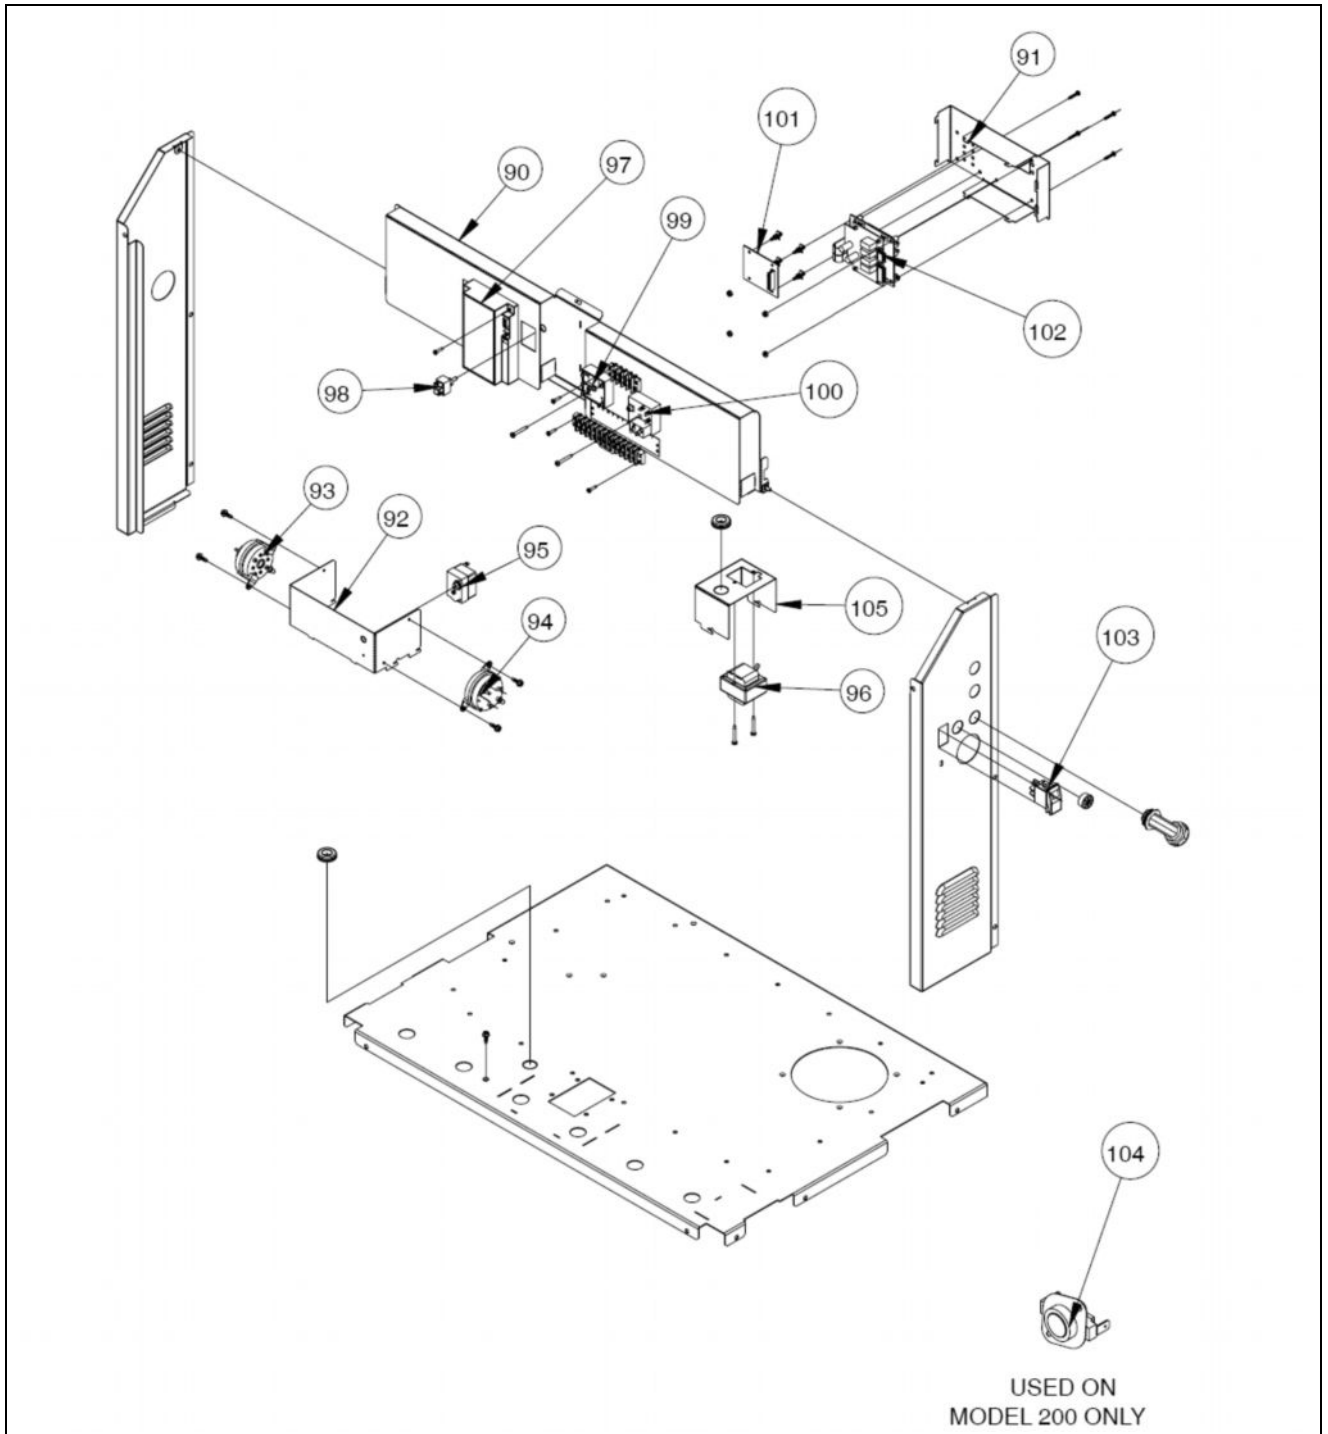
Детали блока управления Пеннант, типоразмеры 200 – 400.
